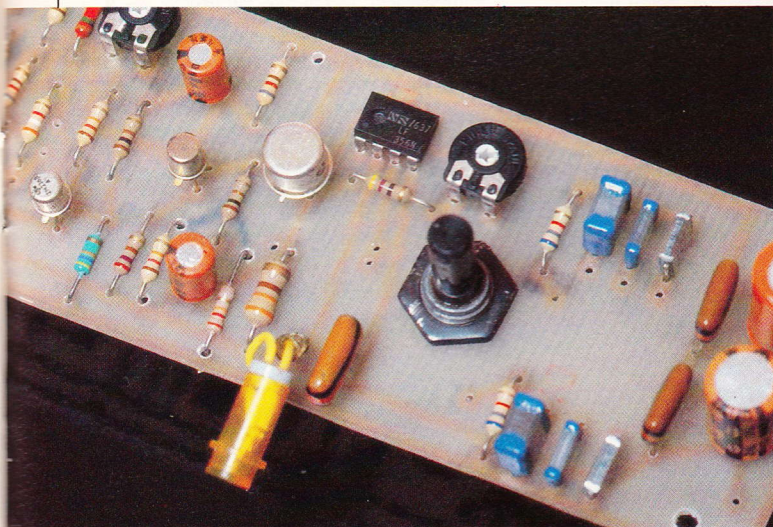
Gros plan sur l'ampoule miniature 6 V, 40 mA.
